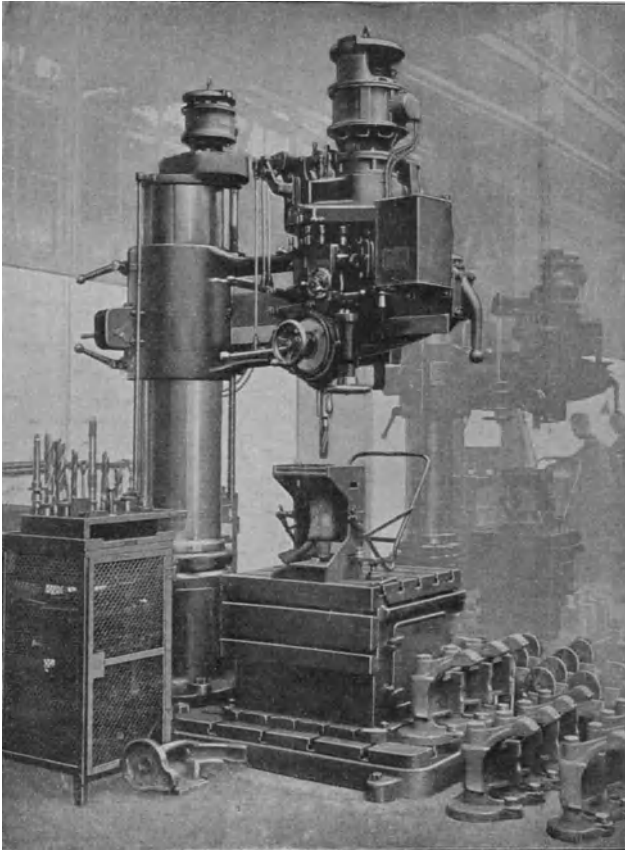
Bohren von Schneckengehäusen in einer Vorrichtung unter der Radialbohrmaschine.
